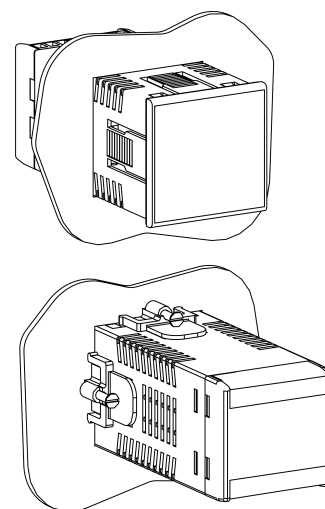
Монтаж прибора щитового крепления Щ5
